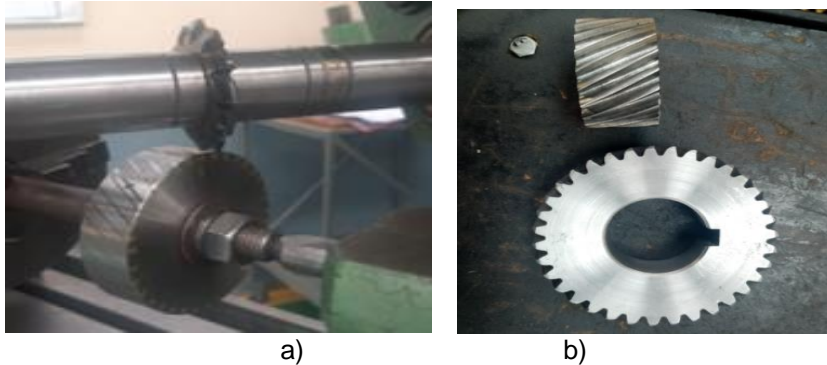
a) Tallado de dientes , b) engranajes helicoidales terminados.
